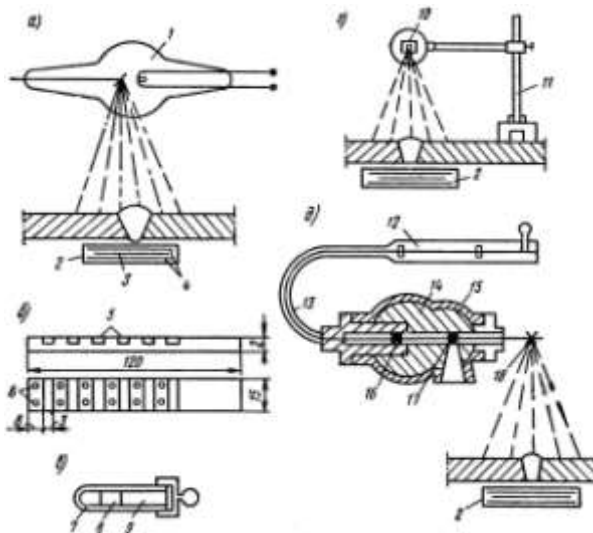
Контроль сварных соединений просвечиванием
